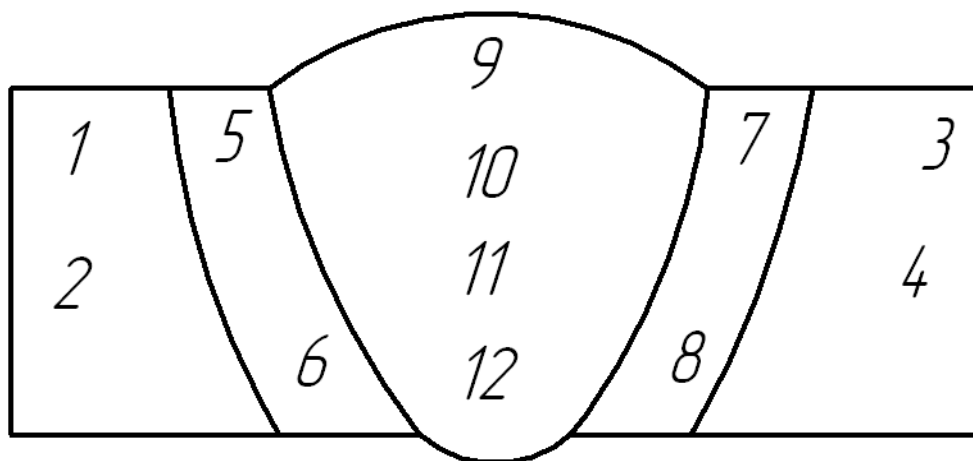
Схема измерения твердости сварного соединения
